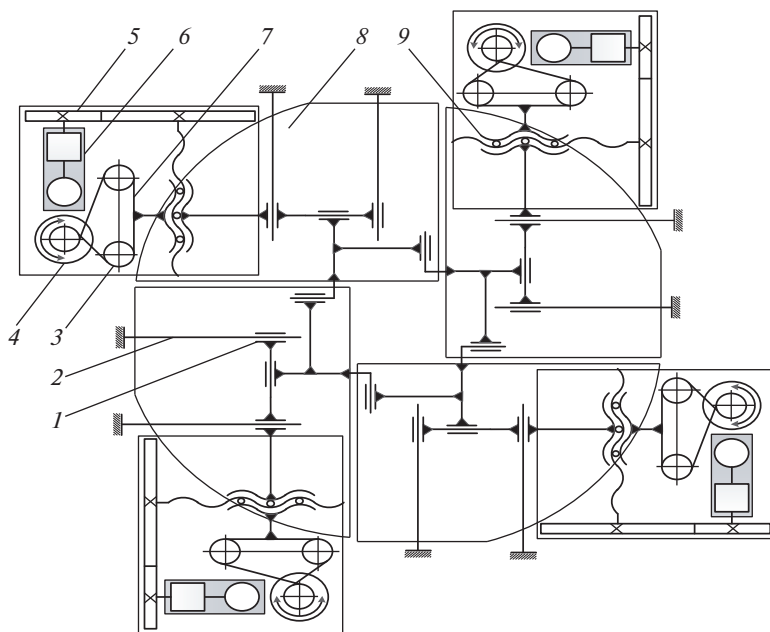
Кинематическая схема привода диафрагмы. 1 – ползун; 2 – направляющая; 3 – шкив; 4 – энкодер; 5 – шестерня; 6 – мотор-редуктор; 7 – ременная передача; 8 – “камень”; 9 – шариковинтовая пара.
